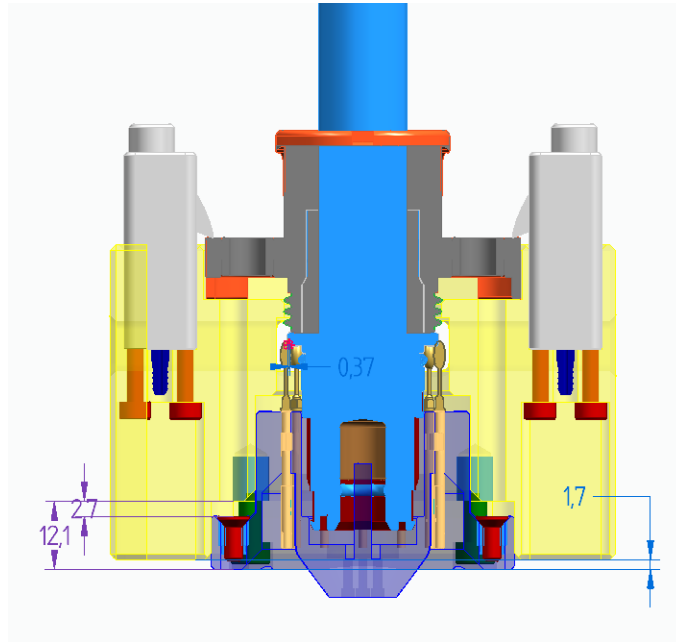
Vista de sección de dispositivo de prueba con conector
